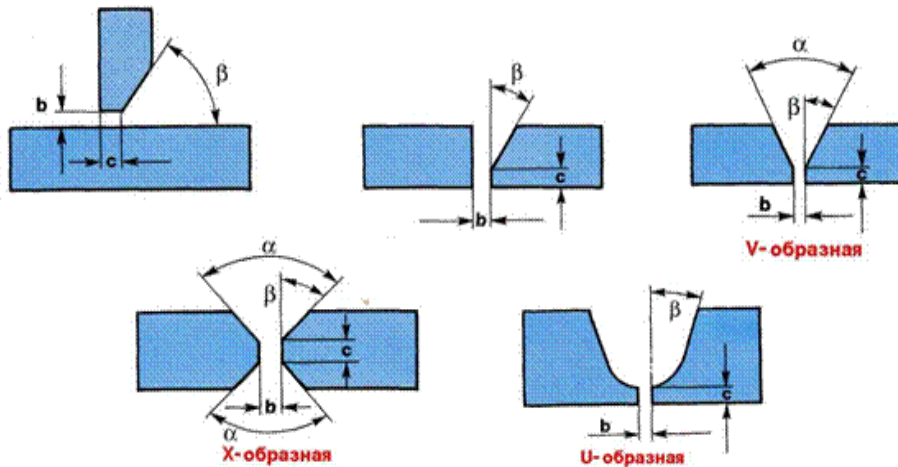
Конструктивные элементы сварных соединений
